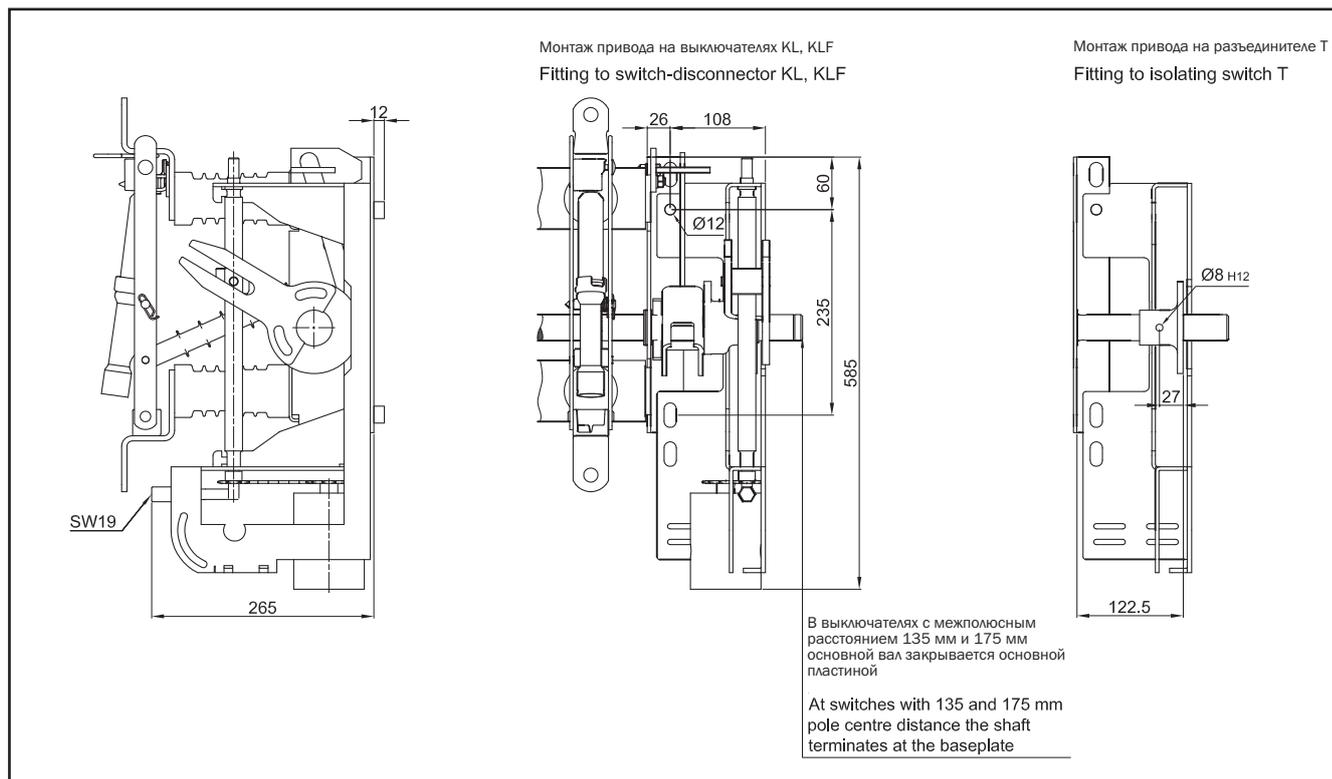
Моторный привод для выключателей до 17,5 кВ
